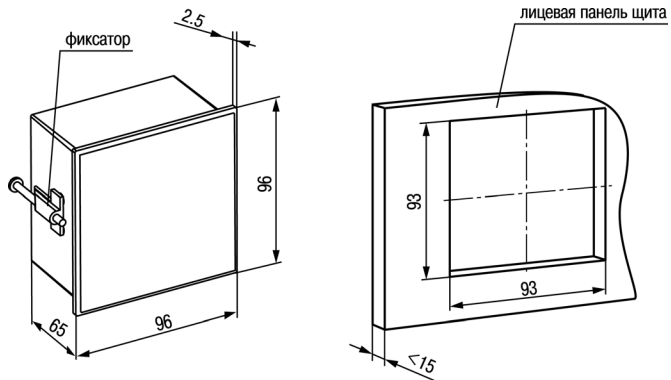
Габаритные размеры корпуса Щ1
